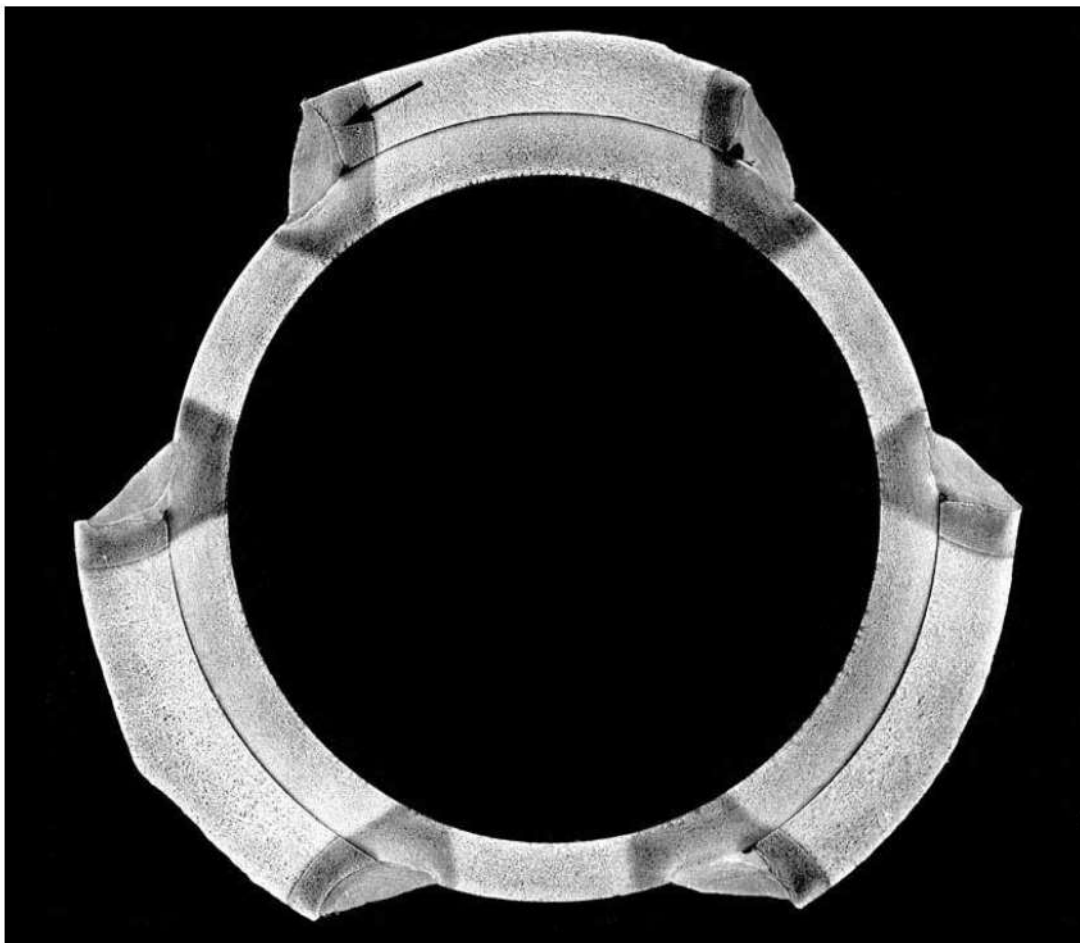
Sección longitudinal a través de la soldadura, donde se puede apreciar el inicio de una grieta (flecha) en la separación soldadura-tubo. Se observa también unos granos más gruesos en las zonas próximas de la soldadura, debido al supercalentamiento. La línea de separación entre la región alterada por el calor del soldado y las partes originales es más áspera en el refuerzo y más suave en el tubo. Reactivo de ácido nítrico. 6X
